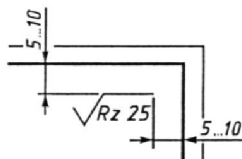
Обозначение одинаковой шероховатости для всех поверхностей
